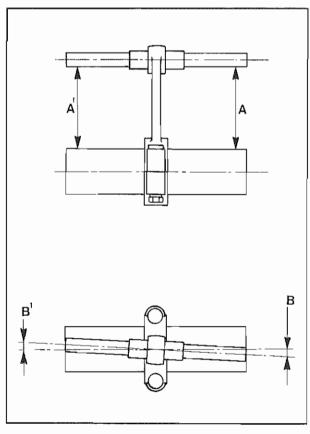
Misurare il parallelismo Measuring the parallelism
